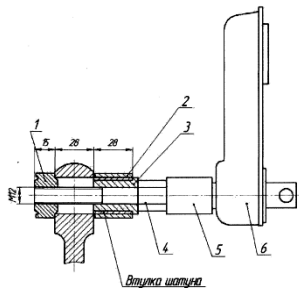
Пристрій для запресування втулки верхньої головки шатуна:
